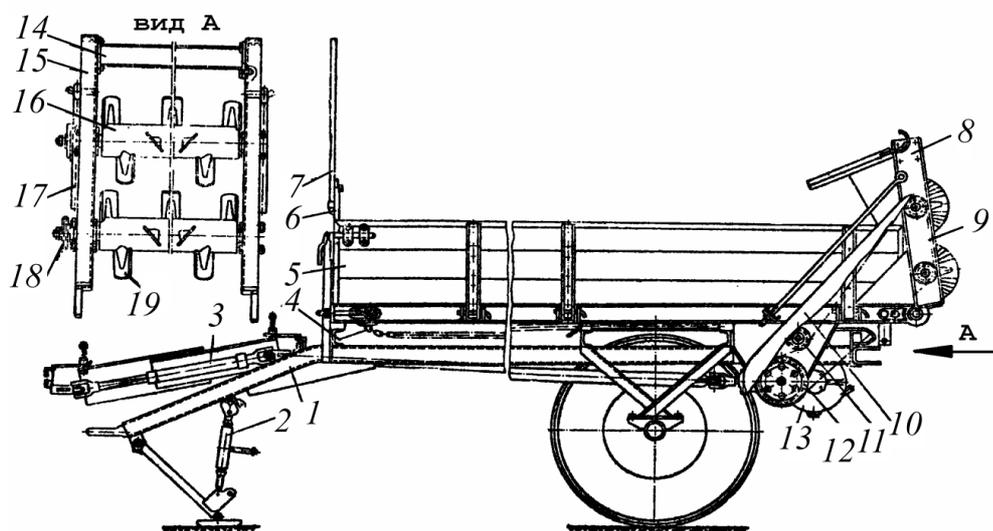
Разбрасыватель прицепной универсальный РПТУ-2М: 1 – рама; 2 – опорная стойка; 3 – карданный привод; 4 – транспортер с платформой; 5 – левый борт; 6 – передний борт; 7 – щиток; 8 – разбрасыватель; 9 – приводная цепь; 10 – защитный кожух; 11 – натяжная звездочка; 12 – привод разбрасывателя; 13 – редуктор; 14 – поперечная балка; 15 – боковина; 16 – барабан; 17 – тяга; 18 – звездочка; 19 – лопатка
